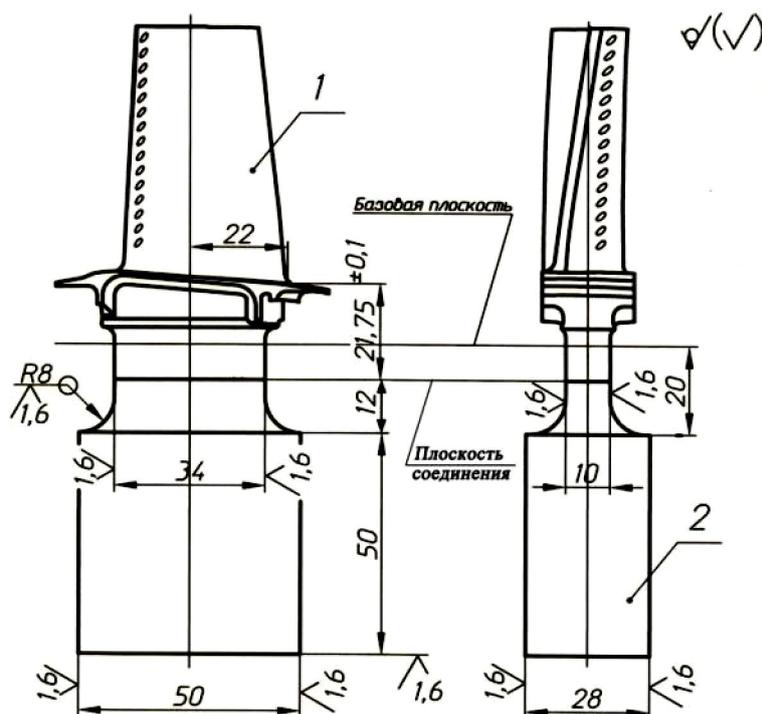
Чертёж образца-имитатора биметаллического моноколеса
